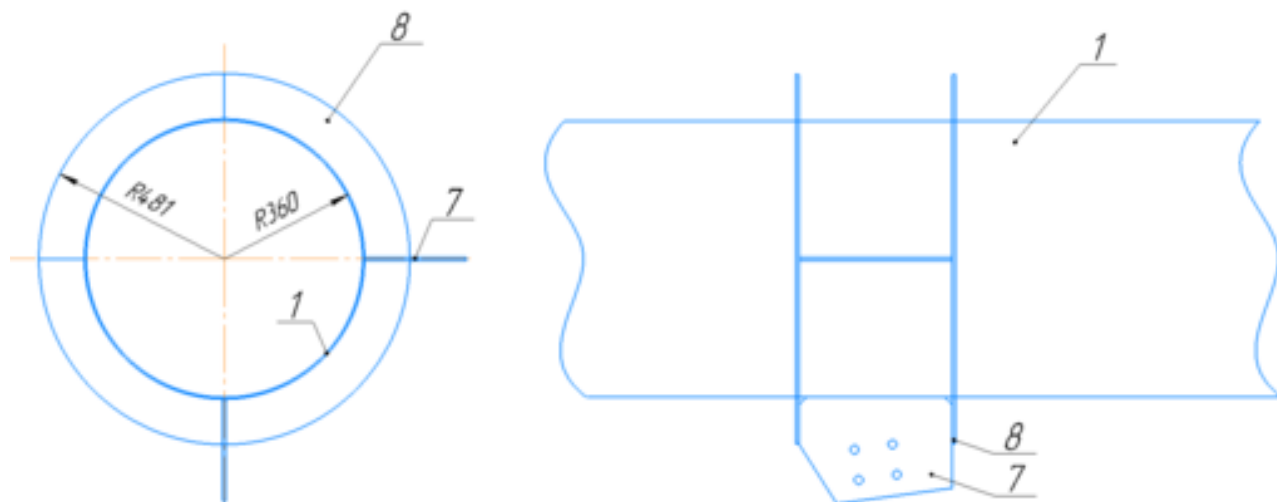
Сварка листов 8 профилем 520x8 с трубой 1 и двумя листами 7
